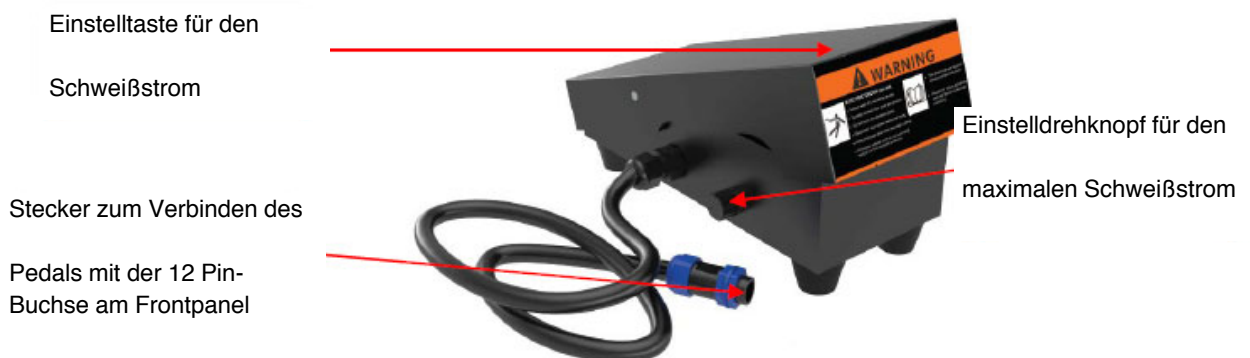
Pedalsteuerung für den Schweißstrom
